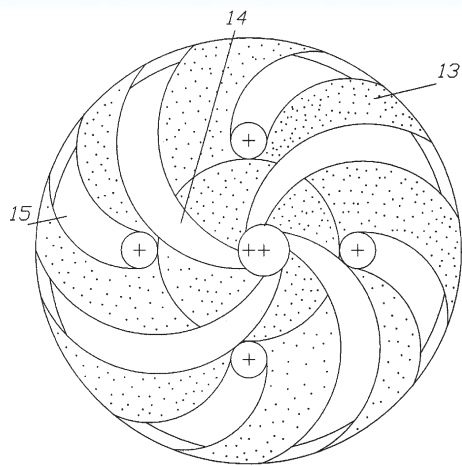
Торцевая поверхность долота с реактивным моментом сил: 13 — ступенчатое долото; 14–15 — канавки цилиндрической формы
